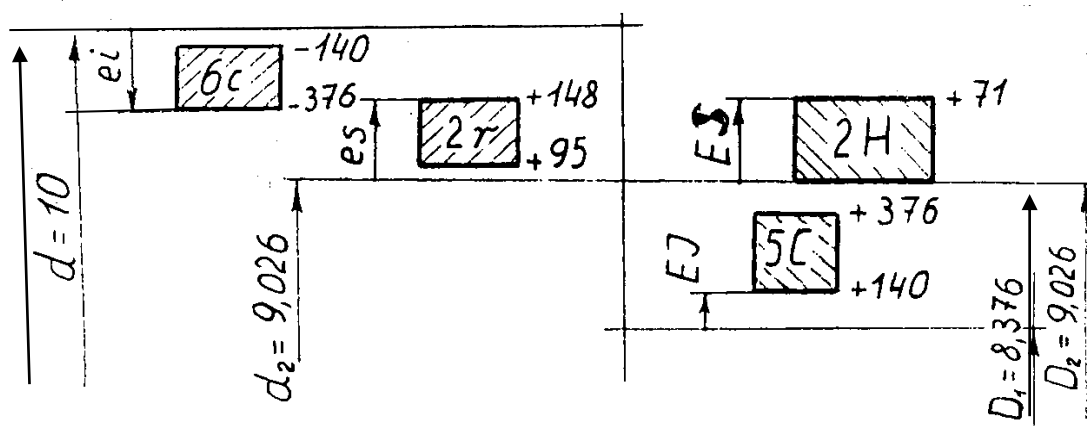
Схема расположения полей допусков метрической резьбы с посадкой с натягом
